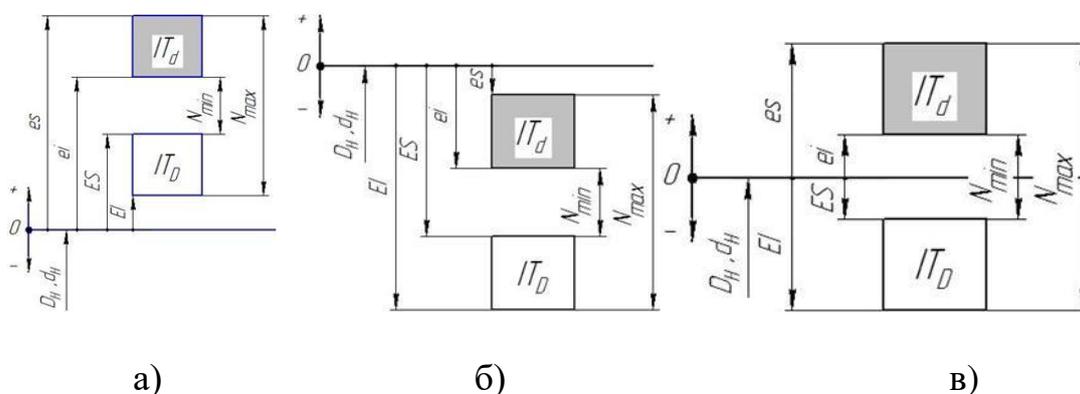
Графическое изображение полей допусков для посадок с натягом: а - отклонения размеров отверстия и вала положительные; б - отклонения размеров отверстия и вала отрицательные; в - отклонения размеров вала положительные, отверстия – отрицательные
